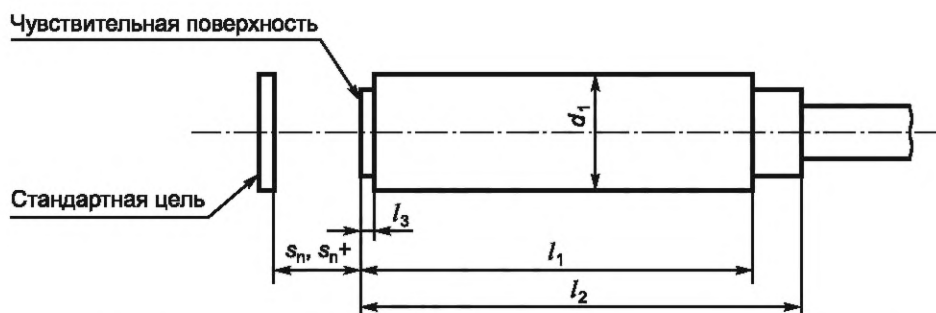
(IB) Габаритные размеры без резьбы на корпусе. Тип кабеля
